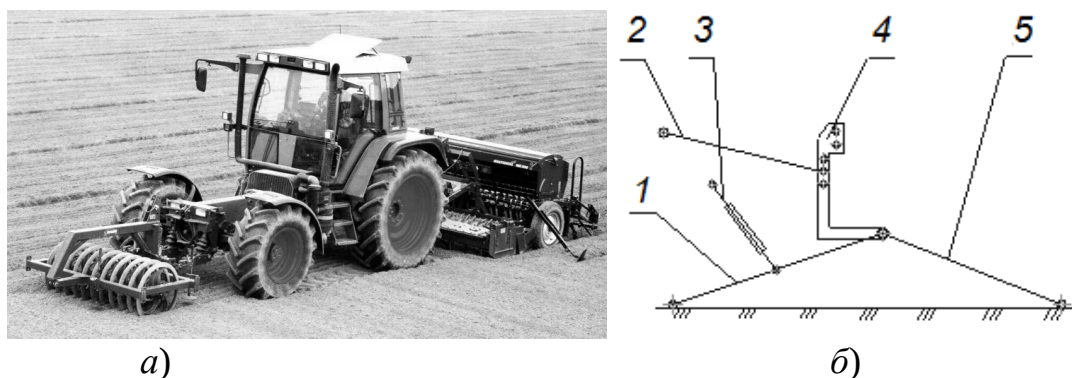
Фронтальний начіпний пристрій для самохідного шасі: а – енергозасіб Fendt 380GHA; б – розроблений начіпний пристрій для самохідного шасі типу Т-16МГ; 1 – поздовжні тяги; 2 – центральна тяга фронтального начіпного пристрою; 3 – вертикальний регульований розкос фронтальної начіпки; 4 – рамка фронтальної начіпки; 5 – розкоси
